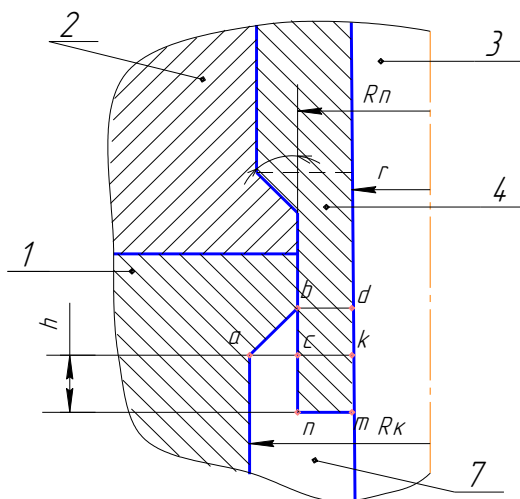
Устройство для многопереходных процессов прессования – сдвига – осадки полой цилиндрической заготовки на гидравлическом прессе усилием 5600 кН
